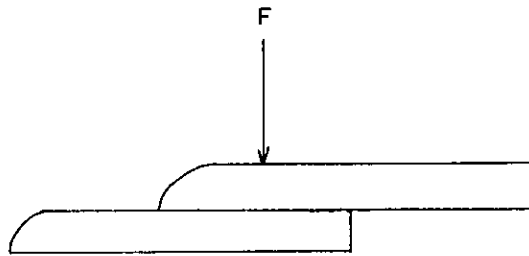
SOLDADURA DE SOLAPA.
